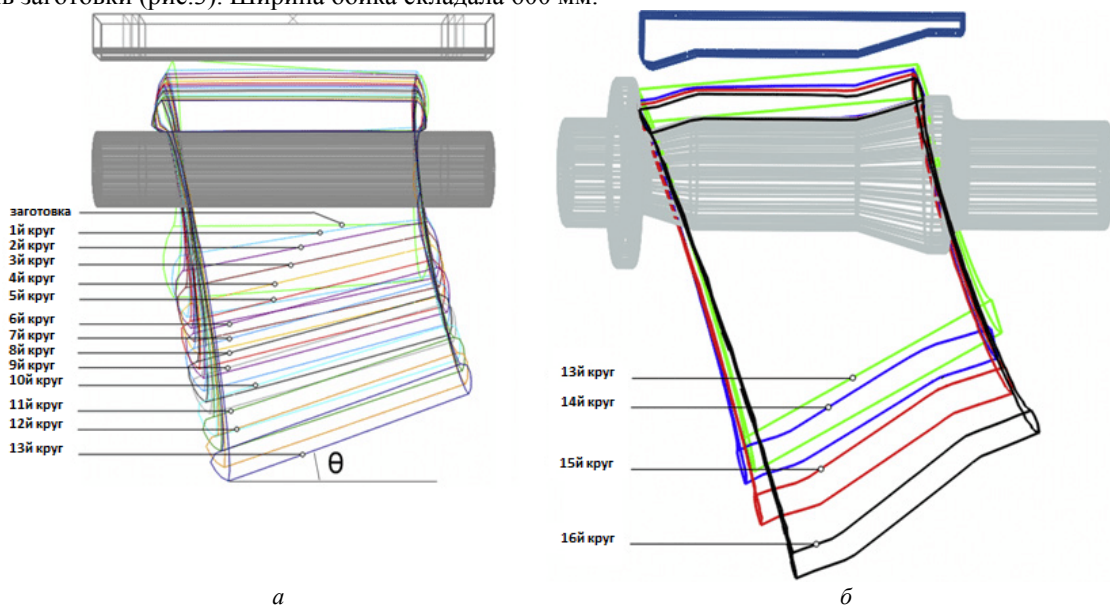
Попереднє (а) та остаточне розкочування (б) при виготовленні конічної обичайки з двома циліндричними прямими ділянками
